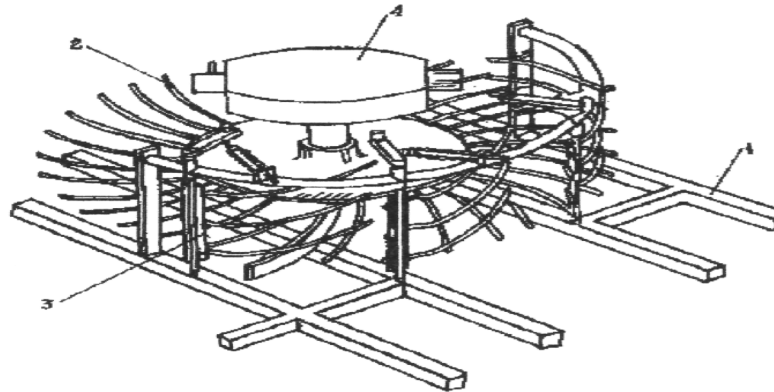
Однороторний очисник: 1 – рама; 2 – очисний ротор; 3 – обмежуючі решітки; 4 – редуктор приводу
